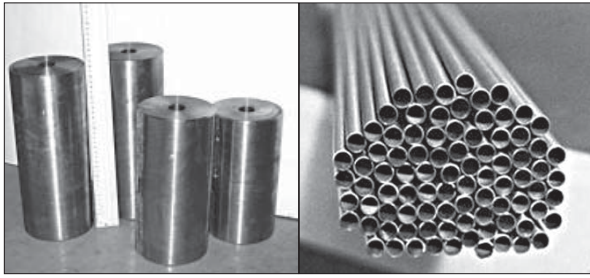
Трубні заготовки та труби, виготовлені зі сплаву Zr1Nb
